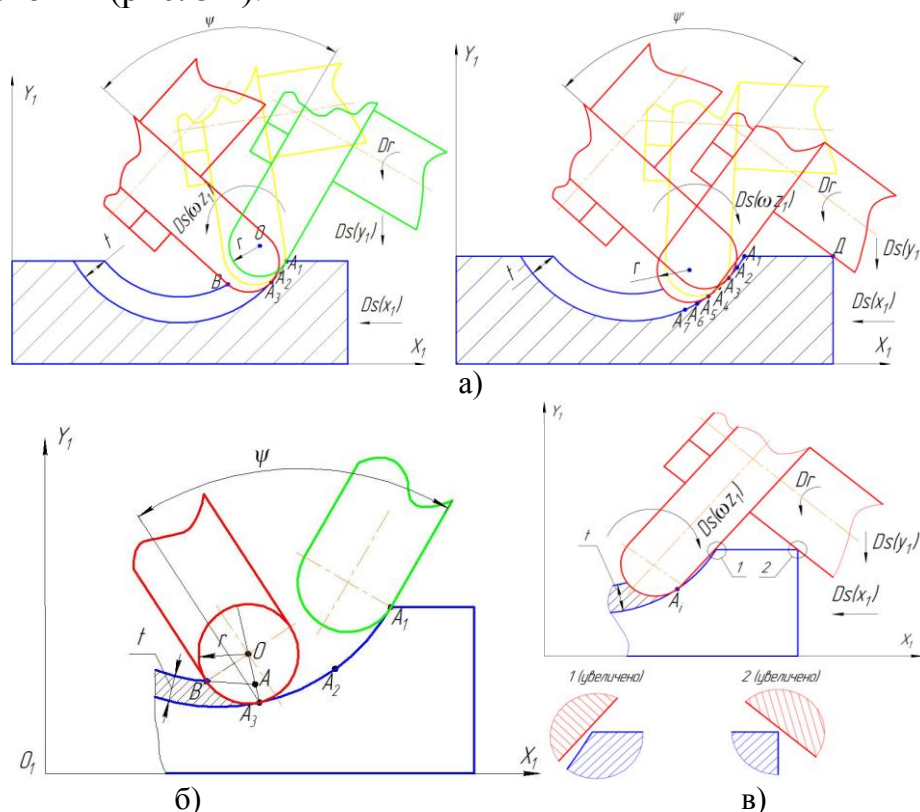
Способ обработки сложных фасонных поверхностей
